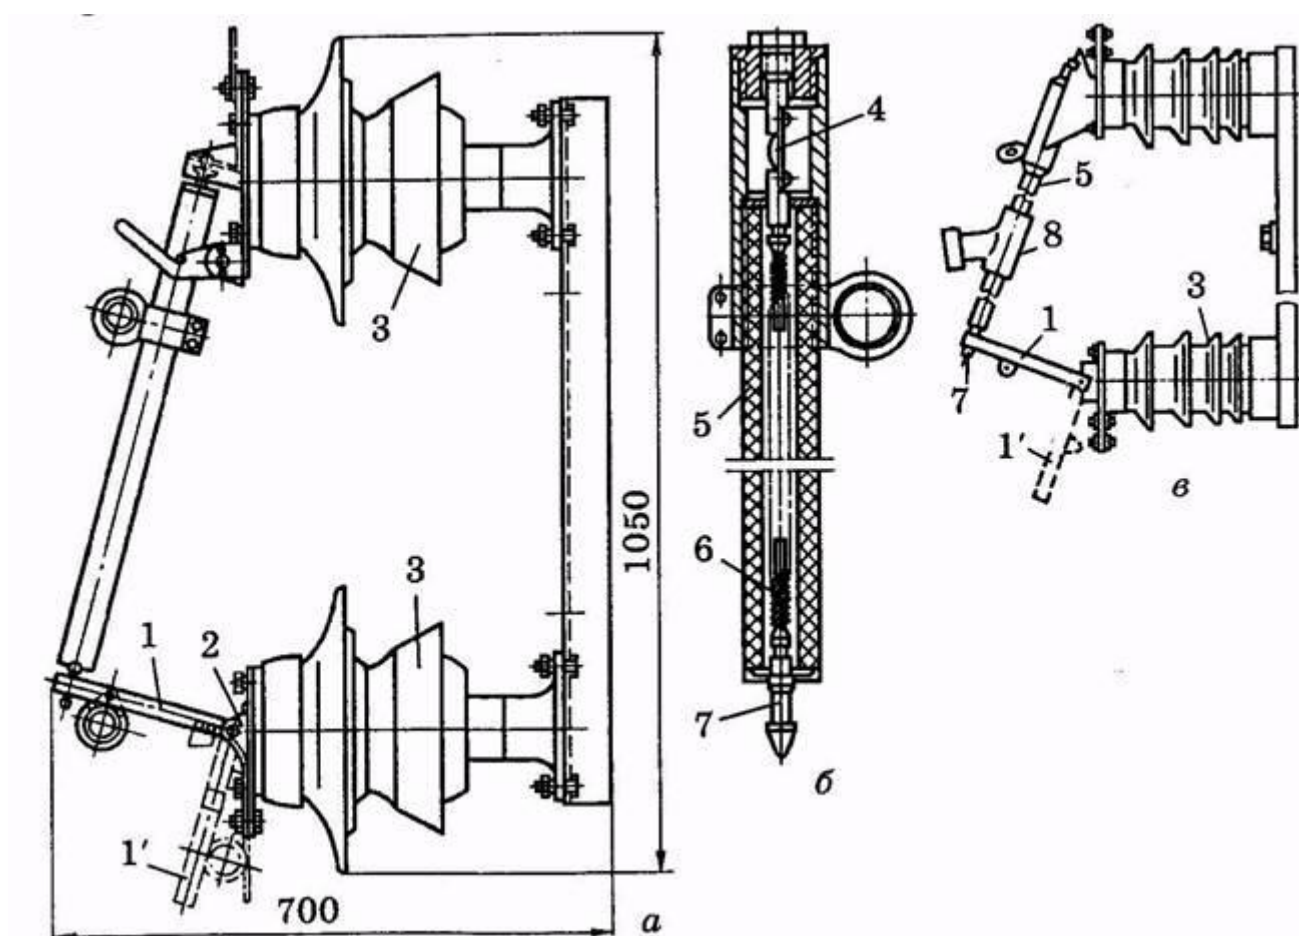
Предохранители типа ПВТ: а, б — общий вид и патрон предохранителя ПВТ-35;
